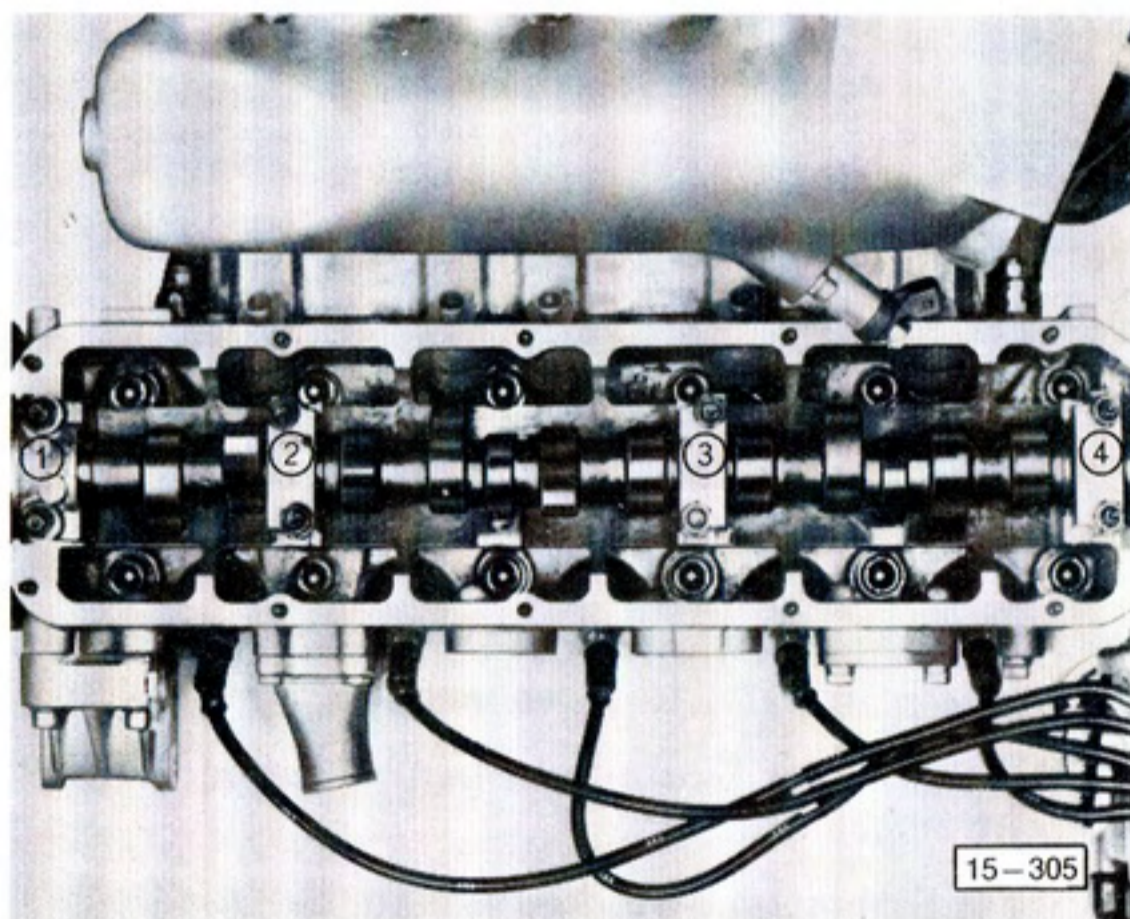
Reihenfolge Lagerdeckel – Nockenwelle einbauen
